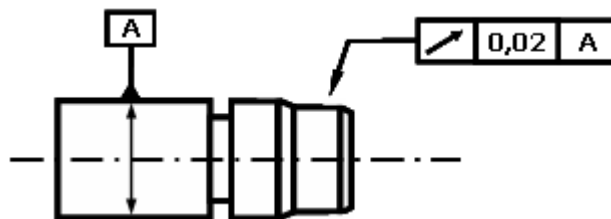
Indicação de tolerância de batida radial em desenho técnico
